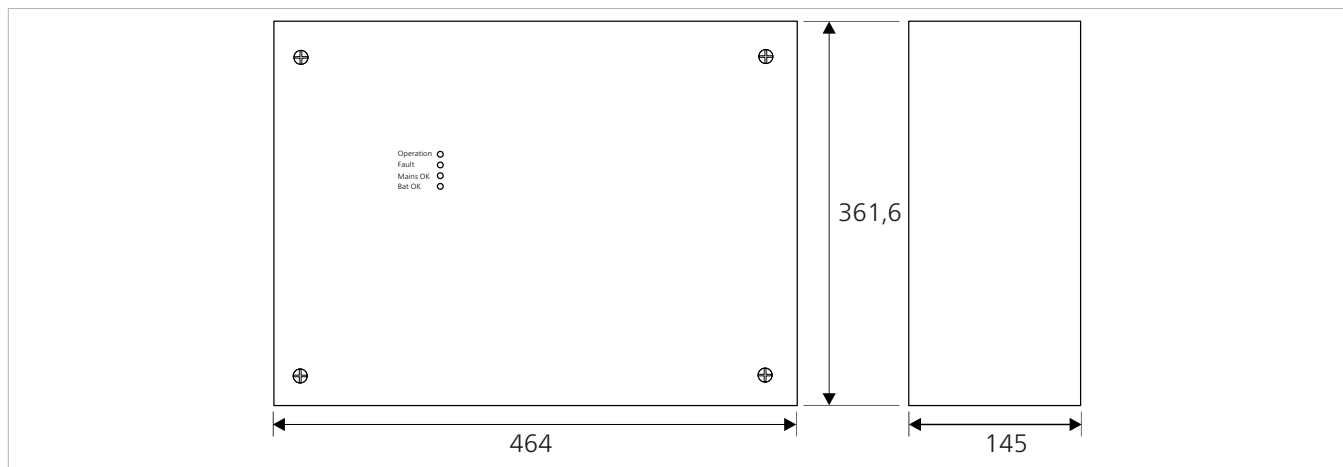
Front- und Seitenansicht BE-PSE03-C
